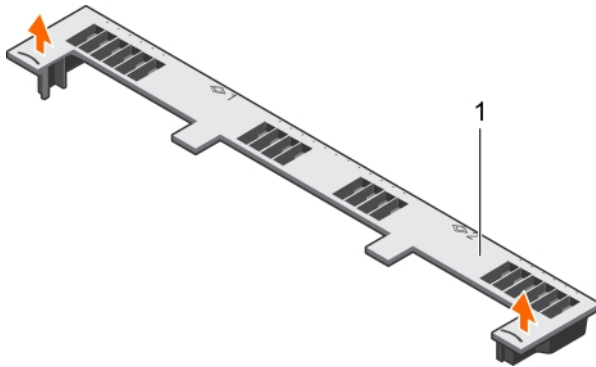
Extracción e instalación de la cubierta de refrigeración
